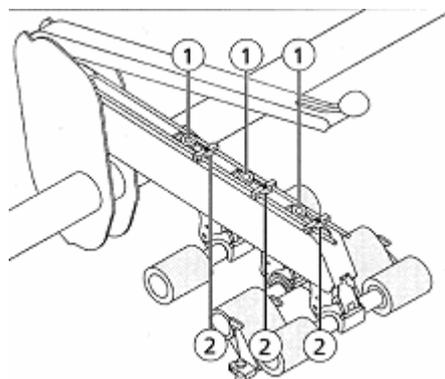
Схема вытяжного прибора ровничной машины Zinser 668
